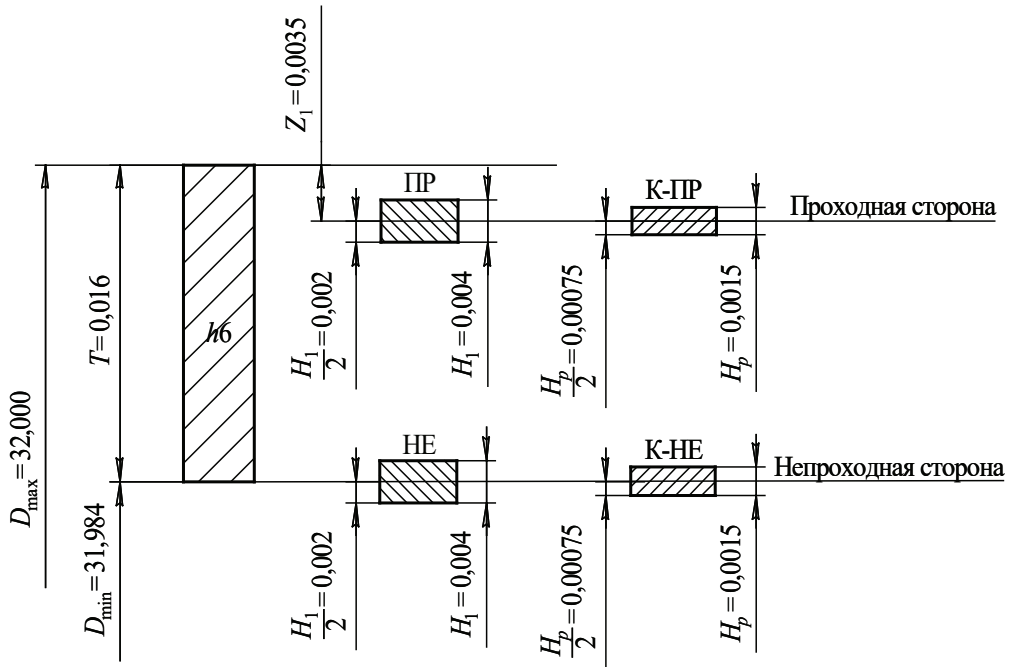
Схема расположения полей допусков рабочих ПР, НЕ и контрольных калибров К-ПР и К-НЕ для вала $\varnothing 32h6_{(-0,016)}$ мм
